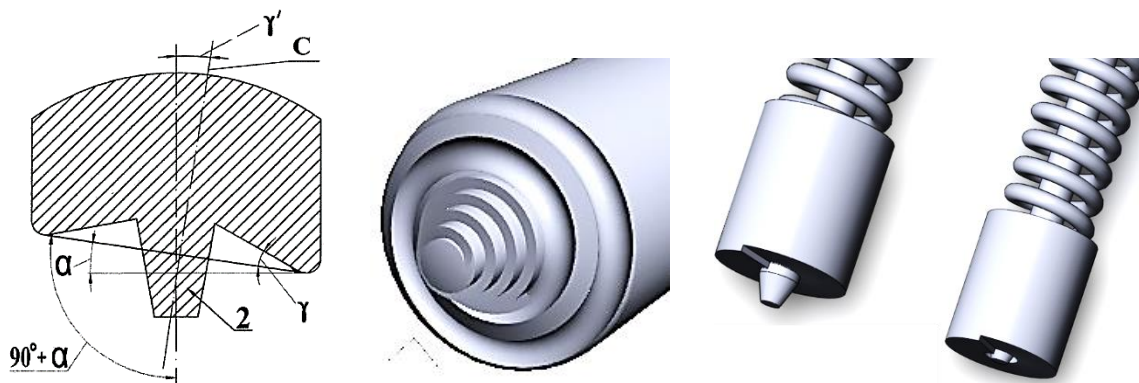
Проекты инструмента прогрессивной конструкции рабочей части
